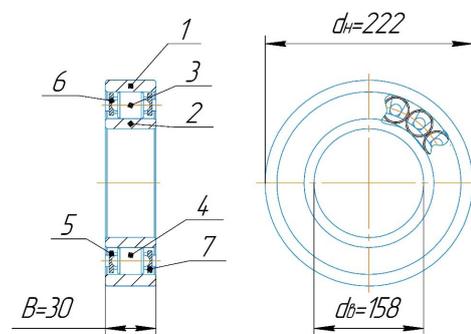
Вид специального роликоподшипника типа 2726 с торцевыми сепараторами: 1 — наружное кольцо; 2 — внутренне кольцо; 3, 4 — тело качения в виде ролика; 5 — сферический элемент координации на торце левого сепаратора (уплотнительной крышки подшипника); 6 — сферический элемент координации на торце ролика; 7 — правый сепаратор (правая уплотнительная крышка подшипника) [6]
